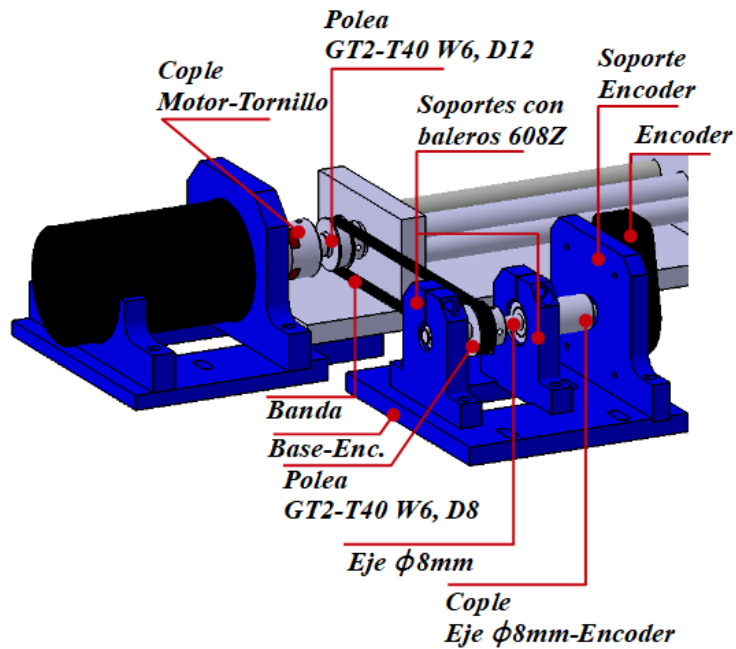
Elementos que forman parte del proceso de medición angular del tornillo.
